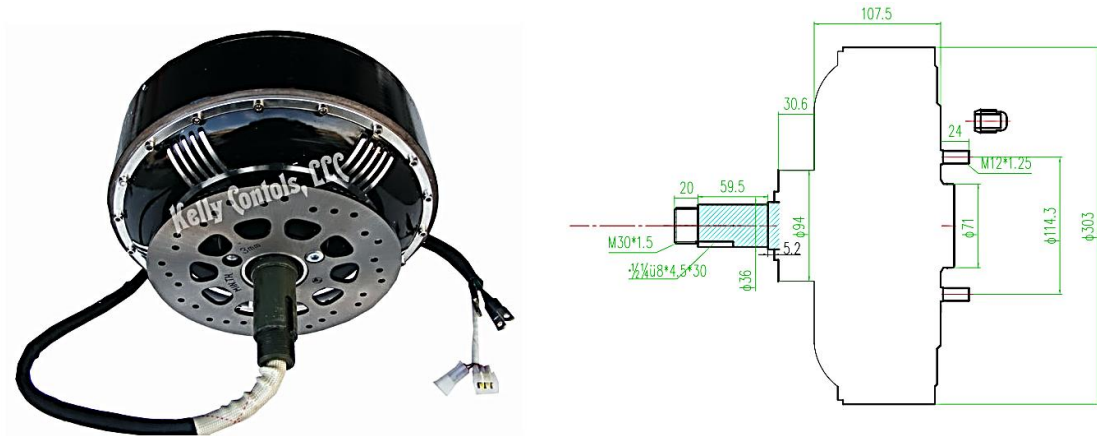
Motor a roda amb rotor extern de 72V i 7000 W - Font: Fitxa tècnica del Car Hub Motor 72V 7KW per Kelly controller, LLC
